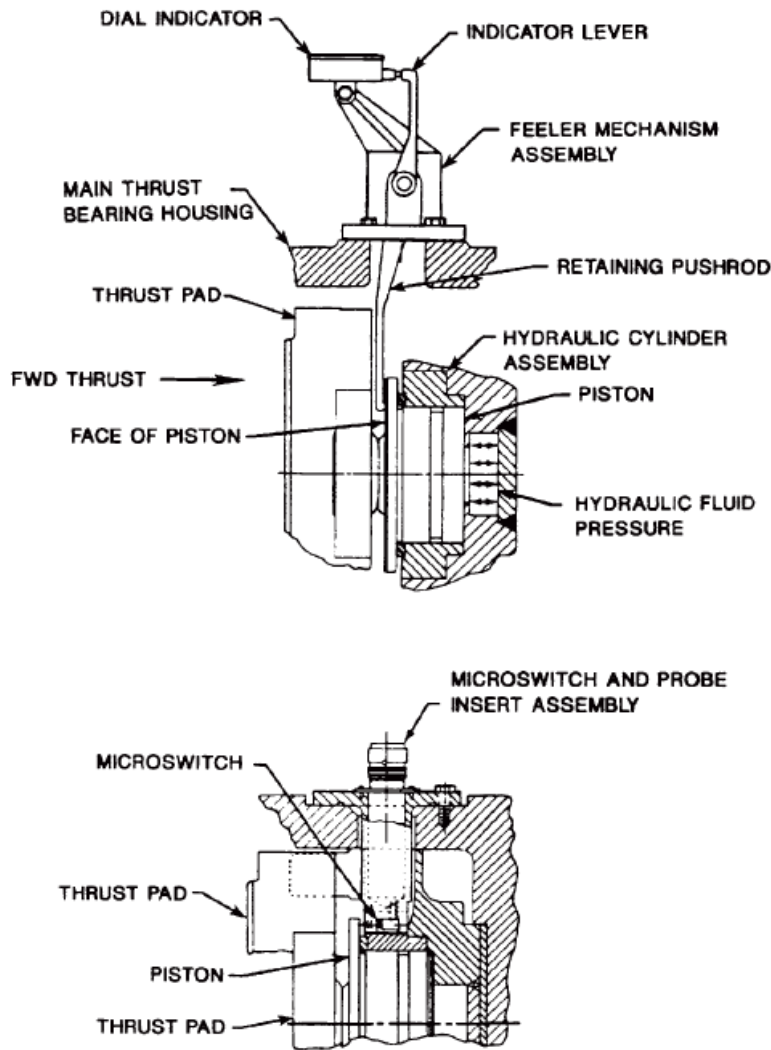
FEELER MECHANISM ASSEMBLY (KINGSBURY)
